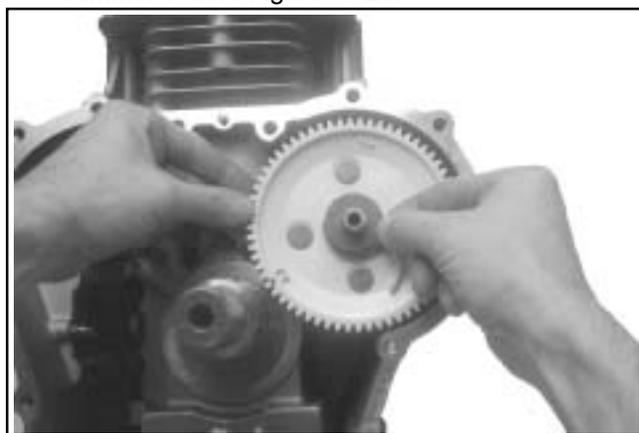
Installazione dell'ingranaggio della camma di scarico.
